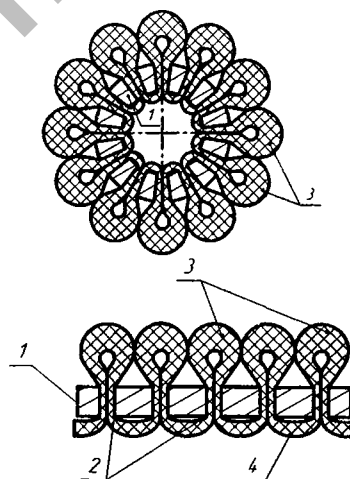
Фильтрующий элемент (пат. 3912 РБ): 1 – каркас; 2 – щели прямоугольного сечения; 3 – гофры; 4 – фильтрующая штора из ВПЯМ или ПВМ
